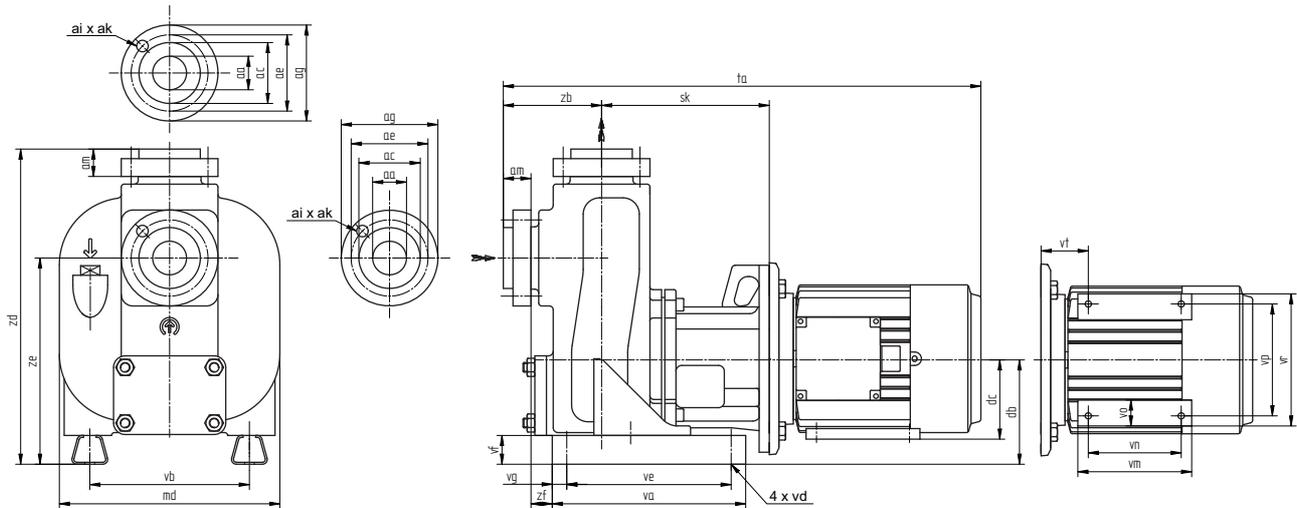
FRES mit ISO 7005 PN20 Anschlüssen.
